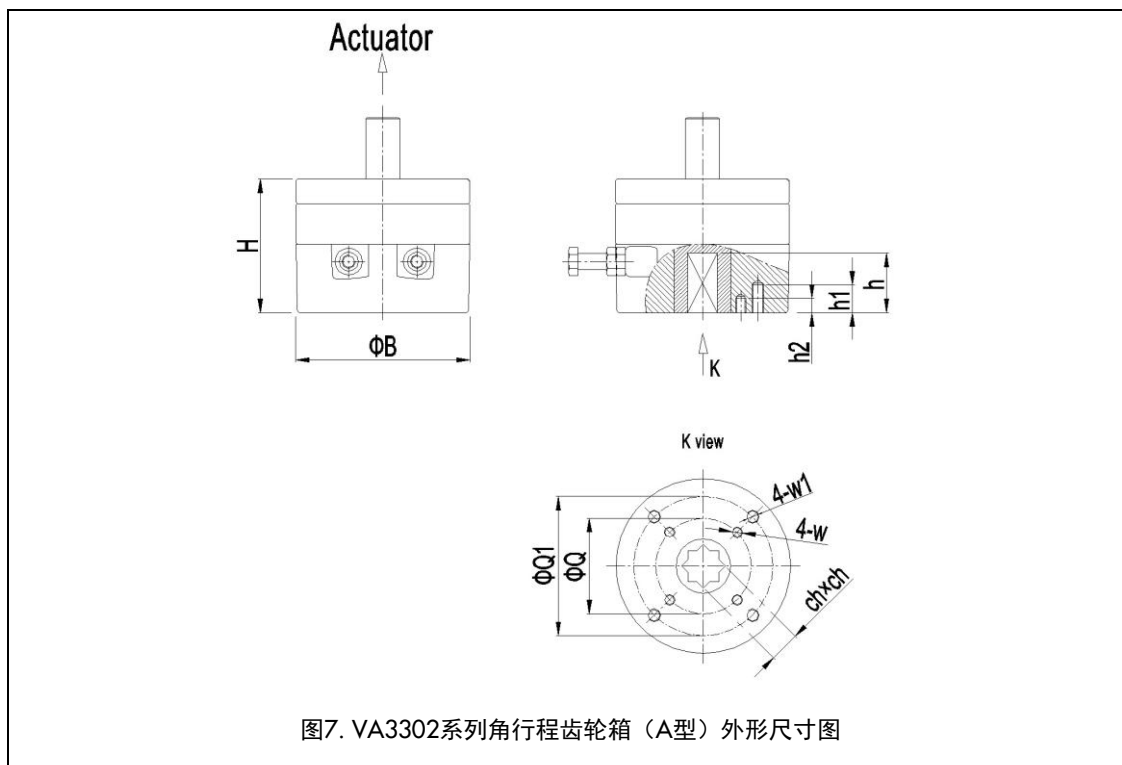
VA3302系列角行程齿轮箱 (A型) 外形尺寸图
